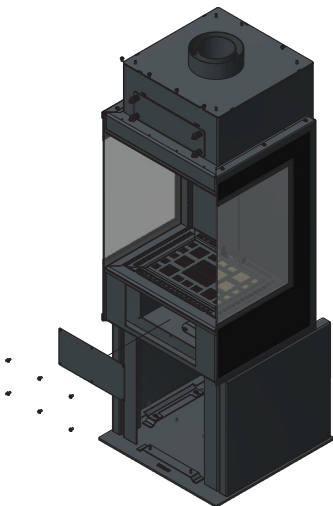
THOR VIEW GAZ - demontaż górnej, dolnej osłony i szyby przedniej
